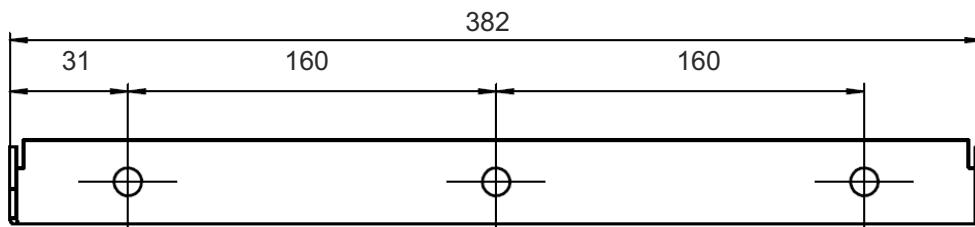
Закладная деталь для крепления ЭВАН PRACTIC -36 ... -120.
